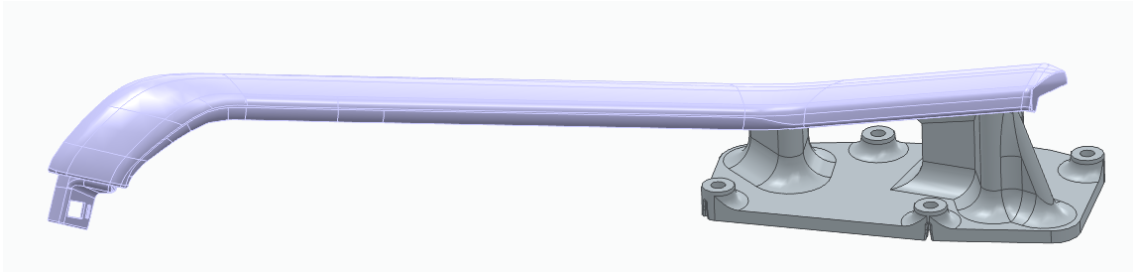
Módulo 2 del utillaje 3 con pieza de trabajo incorporada
